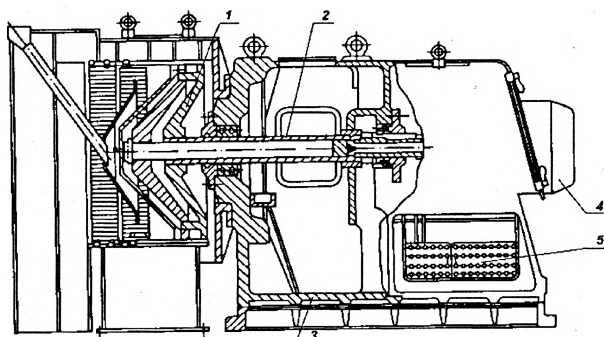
Центрифуга непрерывного действия с горизонтальным расположением ротора: 1 — полости, 2 — ротор, 3 — корпус, 4 — двигатель, 5 — устройство фильтрации
